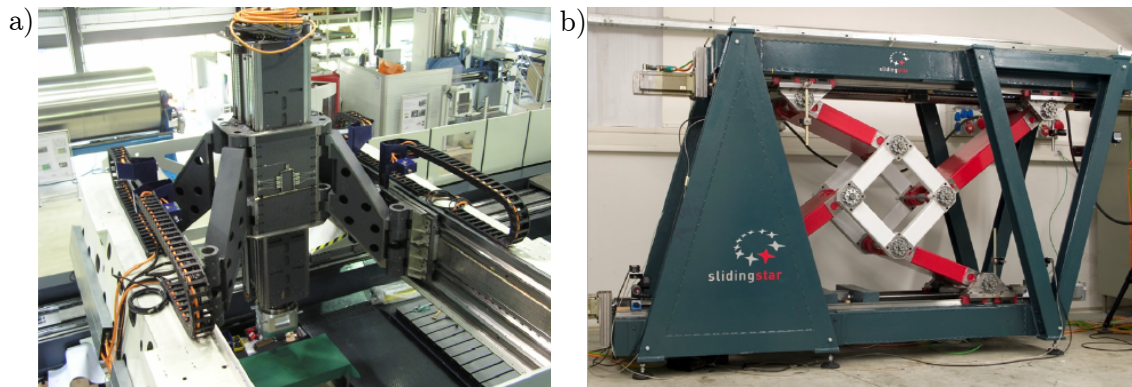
Redundant angetriebene Werkzeugmaschinen: a) Redundante Scherenkinematik (Mit freundlicher Genehmigung des Fraunhofer Institut für Werkzeugmaschinen und Umformtechnik (IWU)), b) Sliding Star (Mit freundlicher Genehmigung von Prof. Valasek)
